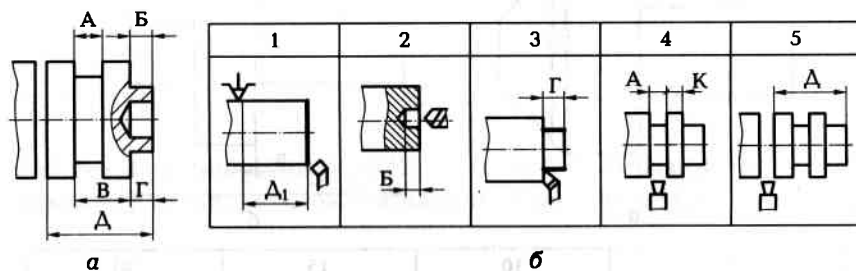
Очередность настройки режущего инструмента на размер:
